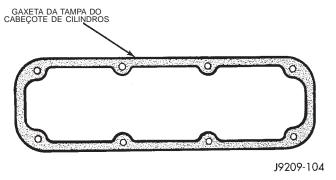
Gaxeta da Tampa do Cabeçote de Cilindros REMOCÃO
